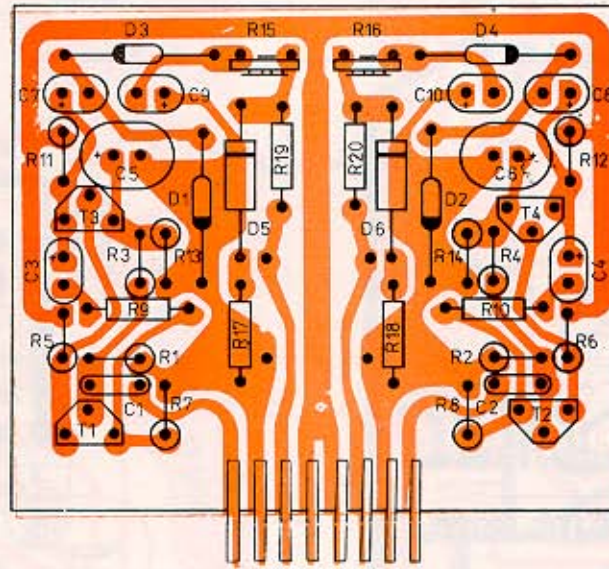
Deska oscilátoru (pohled ze strany spojů)
